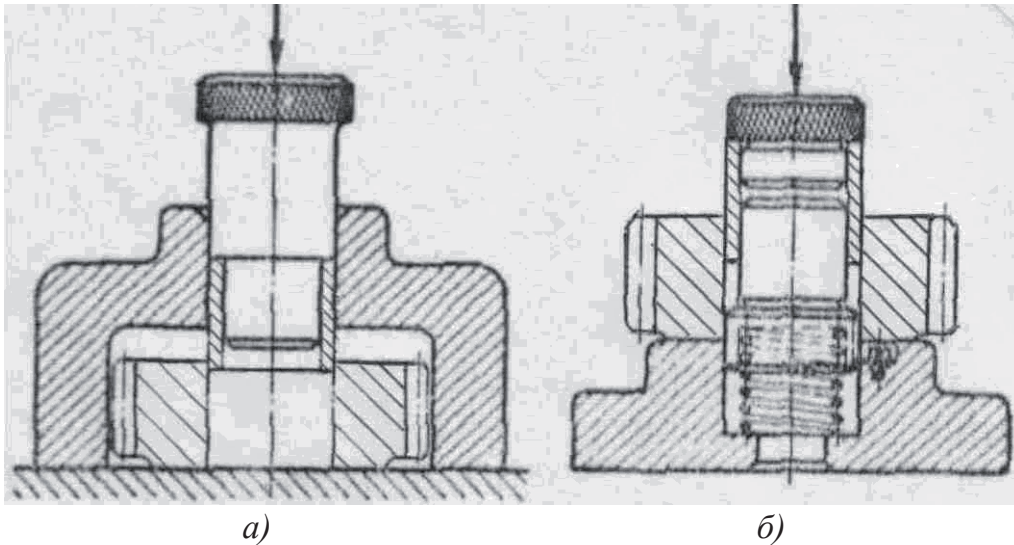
Приспособления для центрирования втулок при их запрессовке в отверстие зубчатого колеса: *а* – центрирование по наружной цилиндрической поверхности; *б* – центрирование по поверхности отверстия
